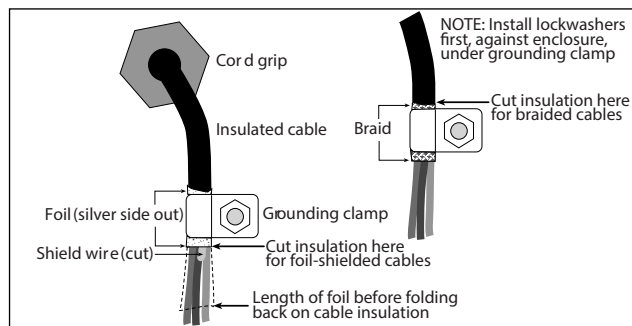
Accesorio de abrazadera de puesta a tierra para cableado apantallado y trenzado
